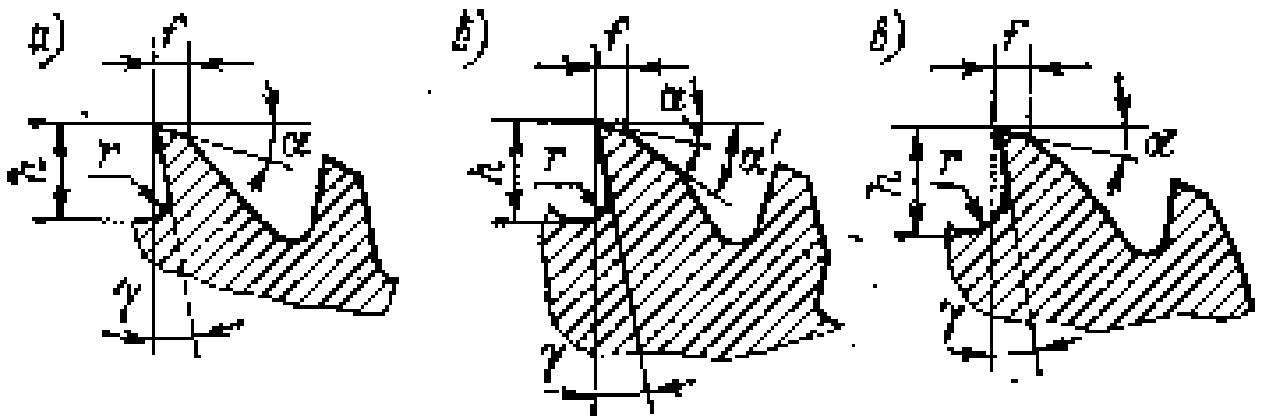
Форми спинки зуба цілісних швидкорізальних фрез
